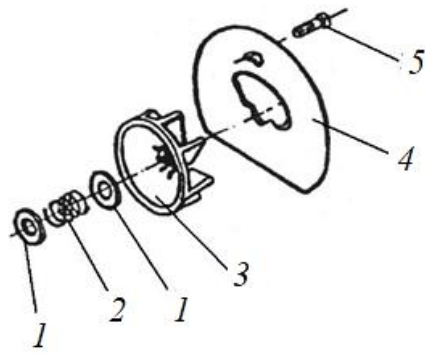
Змінний котушковий пристрій до сівалок типу СУПН-6А:
